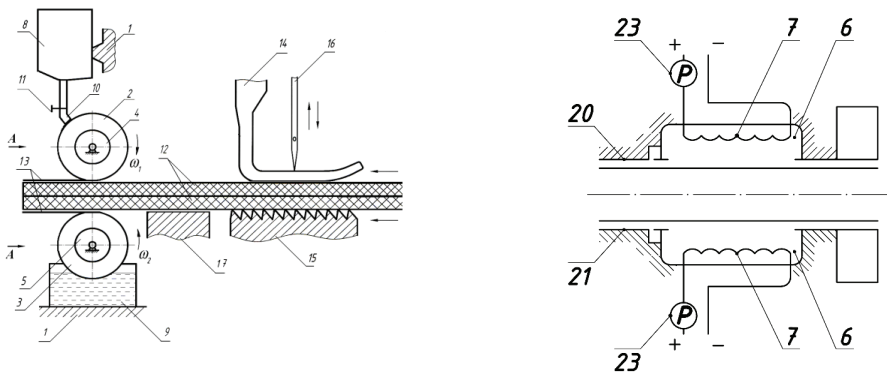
Устройство для нанесения полимерной композиции на детали одежды
